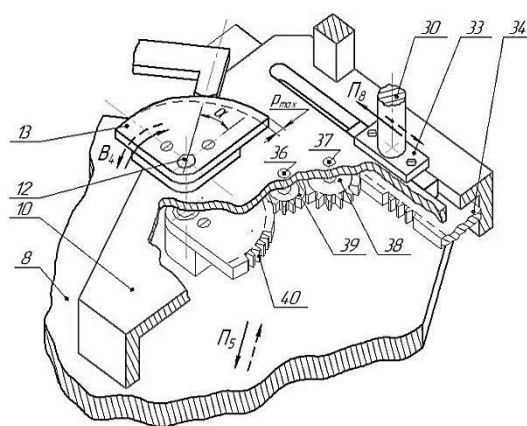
Зубчато-реечный механизм поступательного перемещения упорного пальца:
